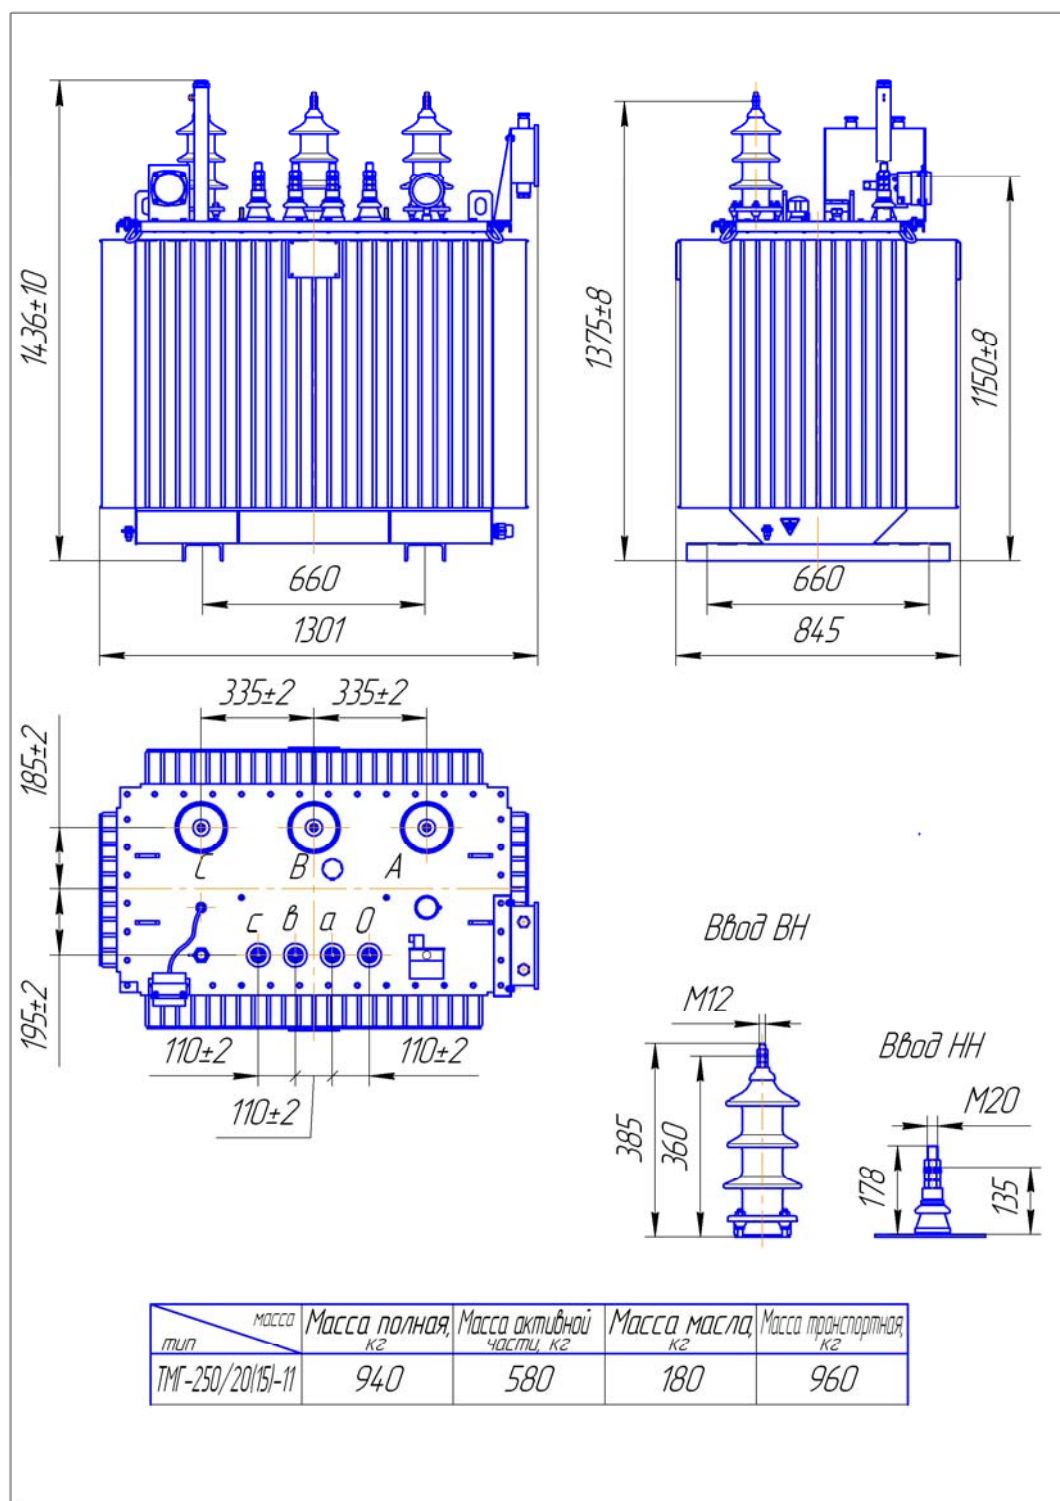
Габаритные, установочные и присоединительные размеры трансформатора ТМГ - 250/20-11
